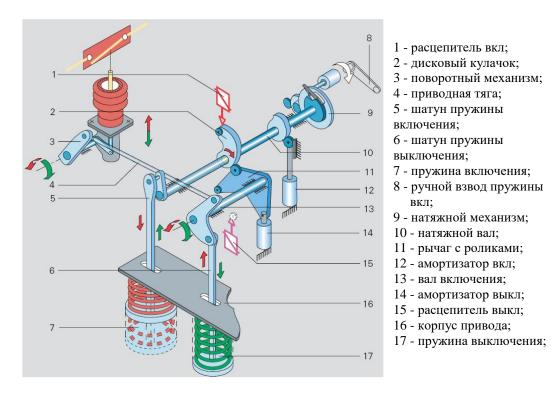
Пружинный привод выключателя 3АР1/2
